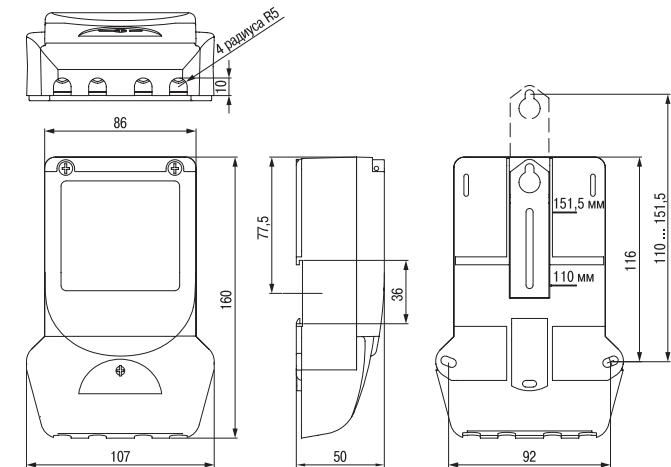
Габаритные и присоединительные размеры счётачиков габарита корпуса 4.
